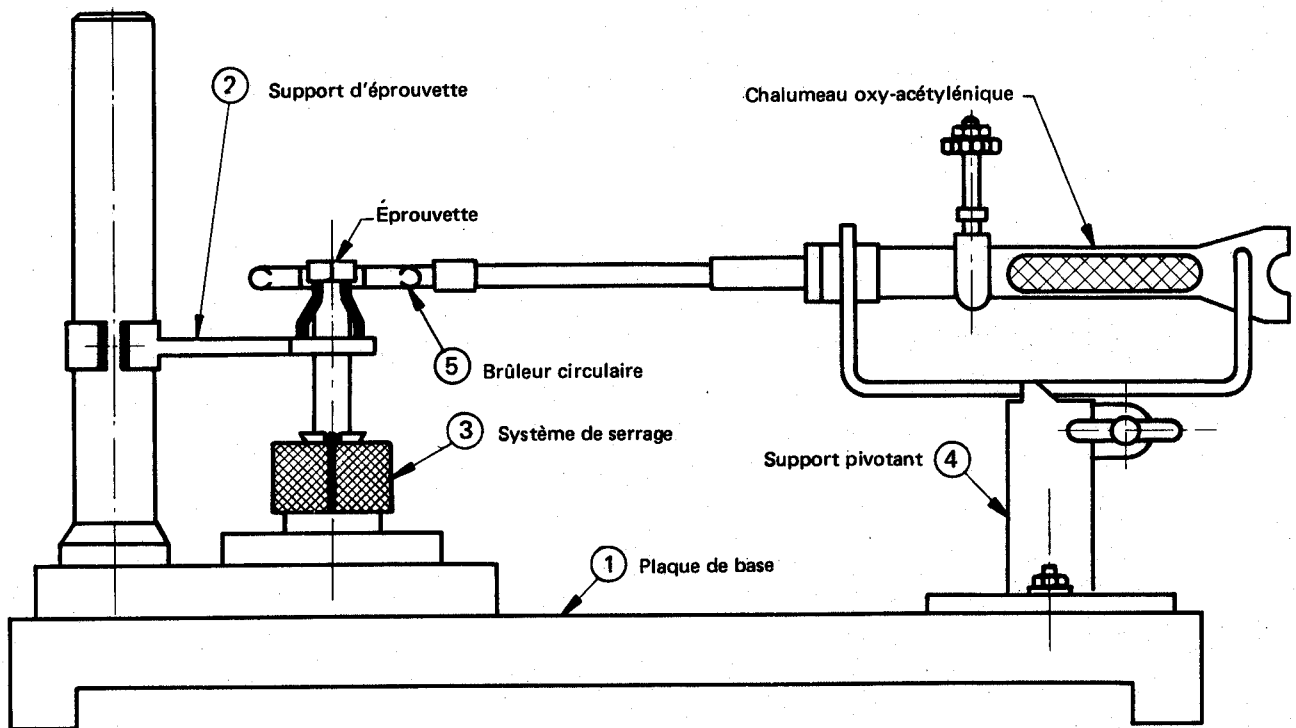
Exemple de montage pour le brasage tendre des éprouvettes
